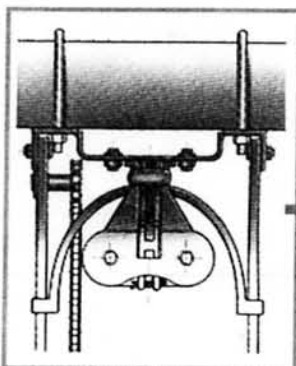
Base de montaje soldada al bastidor que facilita el mantenimiento de la posición de las unidades de siembra
